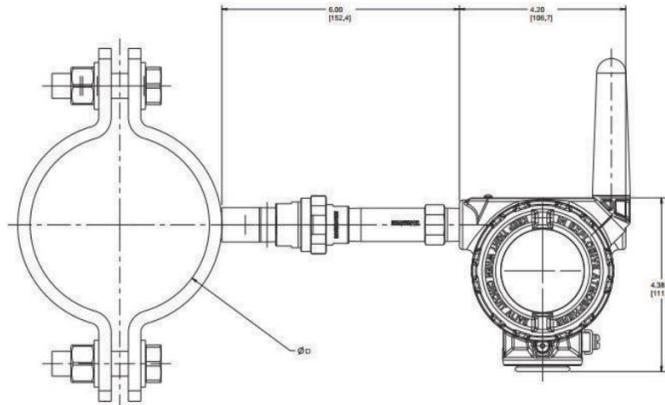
Montaje del sensor 0085 y el transmisor 648
